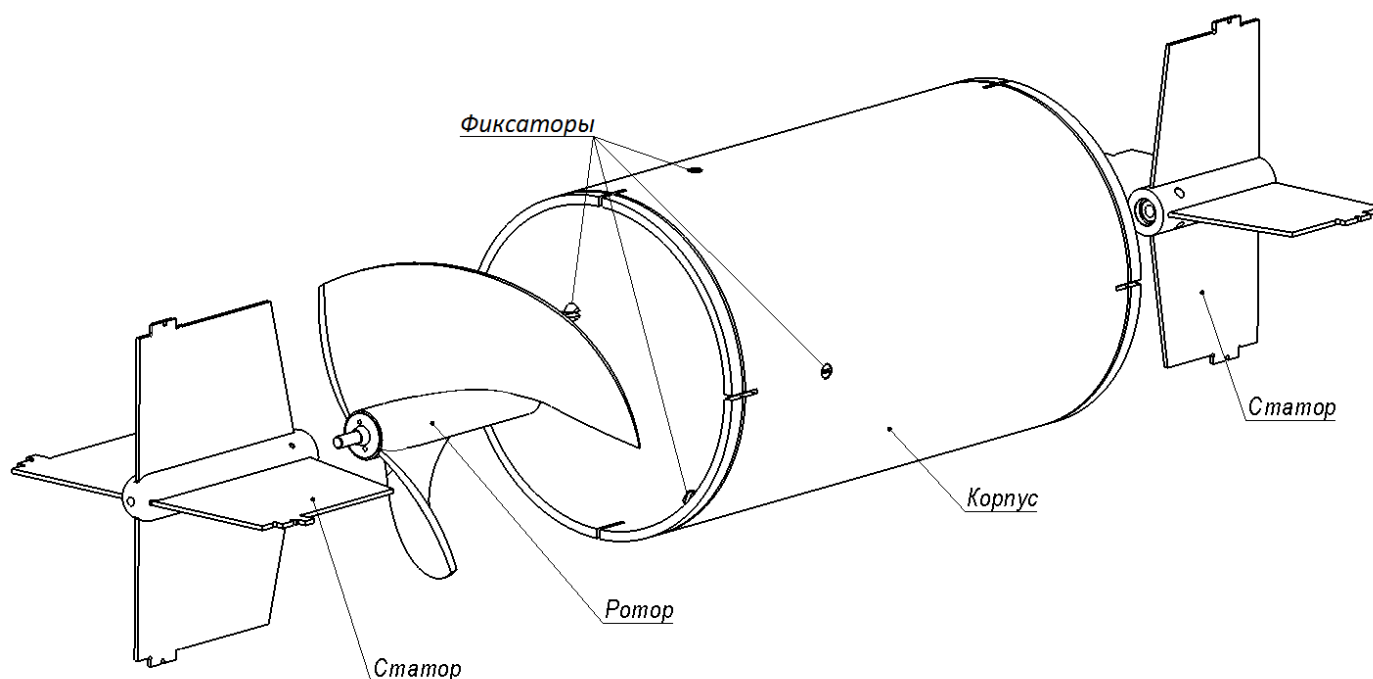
Разборка картриджа «тип Н» Ду250 – основные узлы и детали
